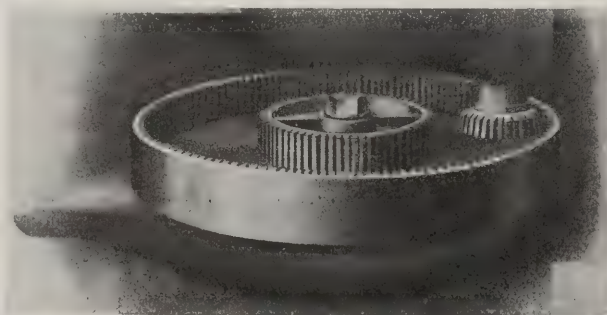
Hobeln von Innen- und Außenverzahnung.
